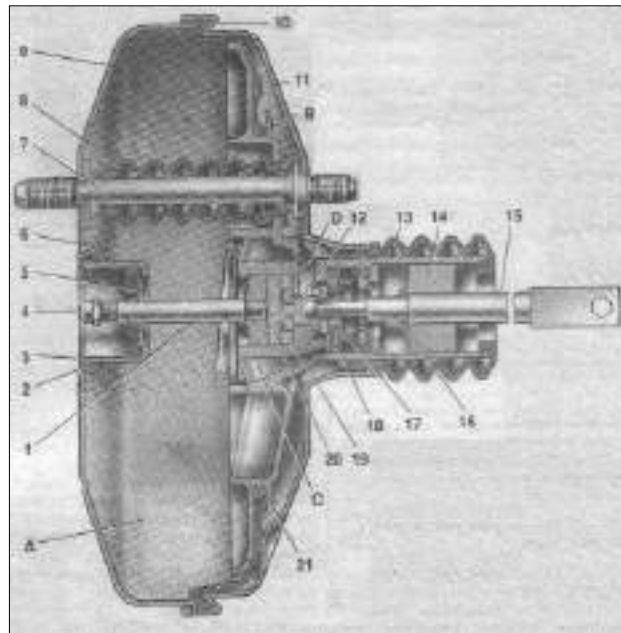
Вакуумний підсилювач: 1 – шток; 2 – ущільнювальне кільце фланця головного циліндра; 3 – чашка корпусу підсилювача; 4 – регулювальний болт; 5 – ущільнювач штока; 6 – зворотна пружина діафрагми; 7 – шпилька підсилювача; 8 – ущільнювальний чохол; 9 – корпус підсилювача; 10 – діафрагма; 11 – кришка корпусу підсилювача; 12 – поршень; 13 – захисний чохол корпусу підсилювача; 14 – повітряний фільтр; 15 – штовхач; 16 – зворотна пружина штовхача; 17 – пружина клапана; 18 – клапан; 19 – втулка корпусу клапана; 20 – буфер штока; 21 – корпус клапана; А – вакуумна камера; В – атмосферна камера; З, D – канали.
